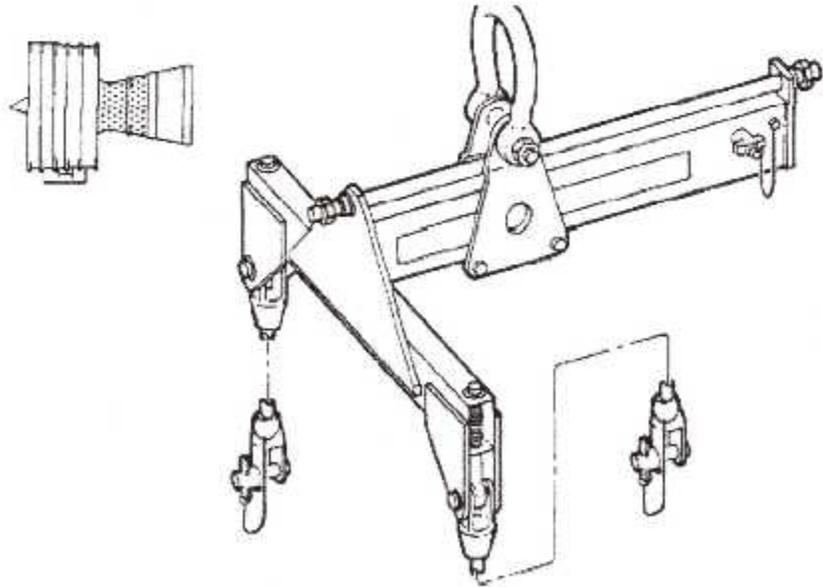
la Poutre de Levage, 856A1107G07.
